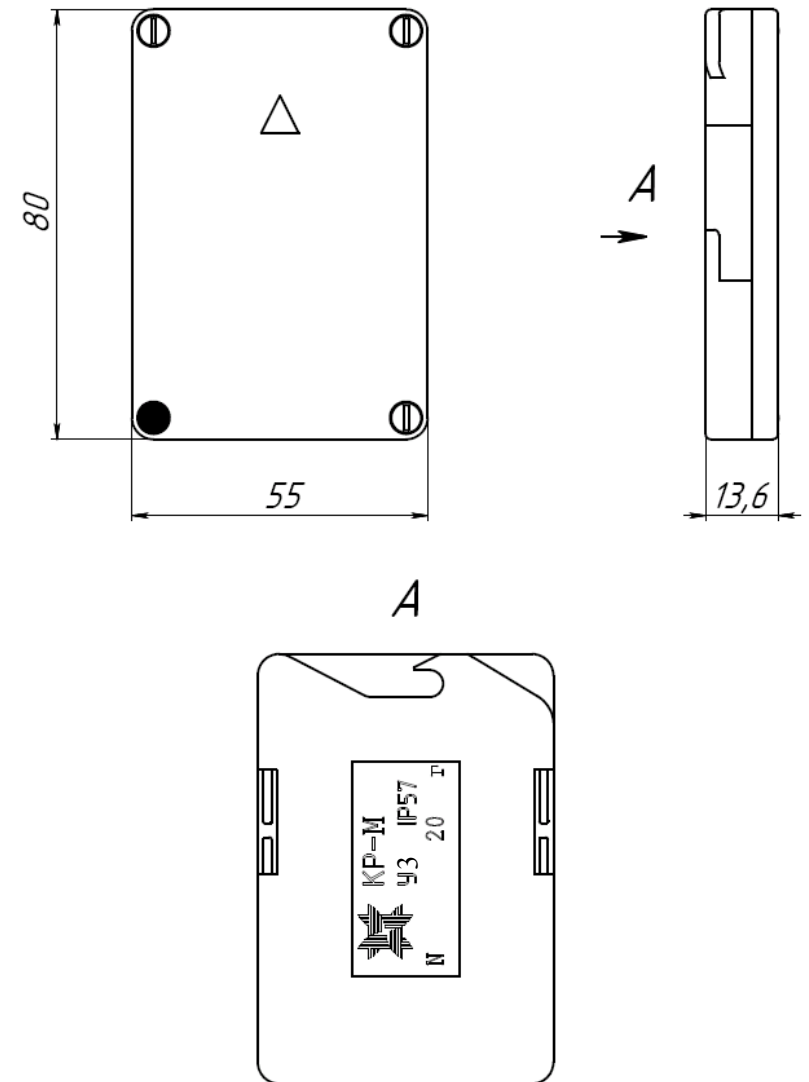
Внешний вид и габаритные размеры кассеты регистрации КР-М 36993-360-00-01
